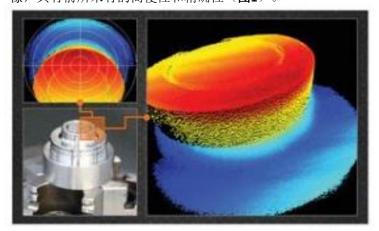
使用LDD-700内联焊接监测系统通过焊接头获取的不锈钢零件3D图像; 3D视频技术可实现焊接激光束与零件的精确对焦。
